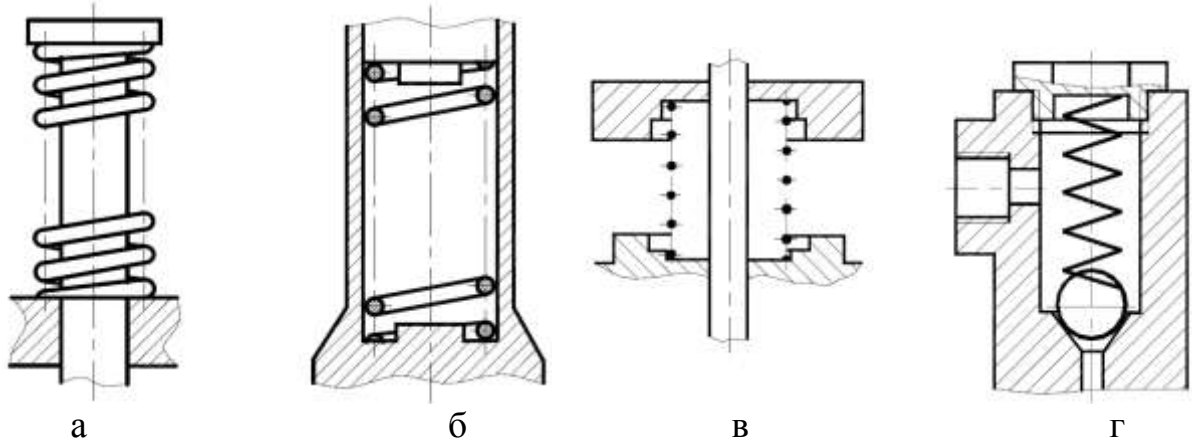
Способы изображения пружин на чертежах общего вида
